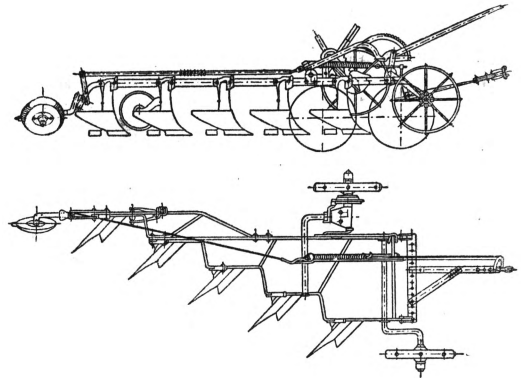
Четырех—пятикорпусный тракторный Л. Ч-25-П. Вид с бороздной стороны и сверху.
